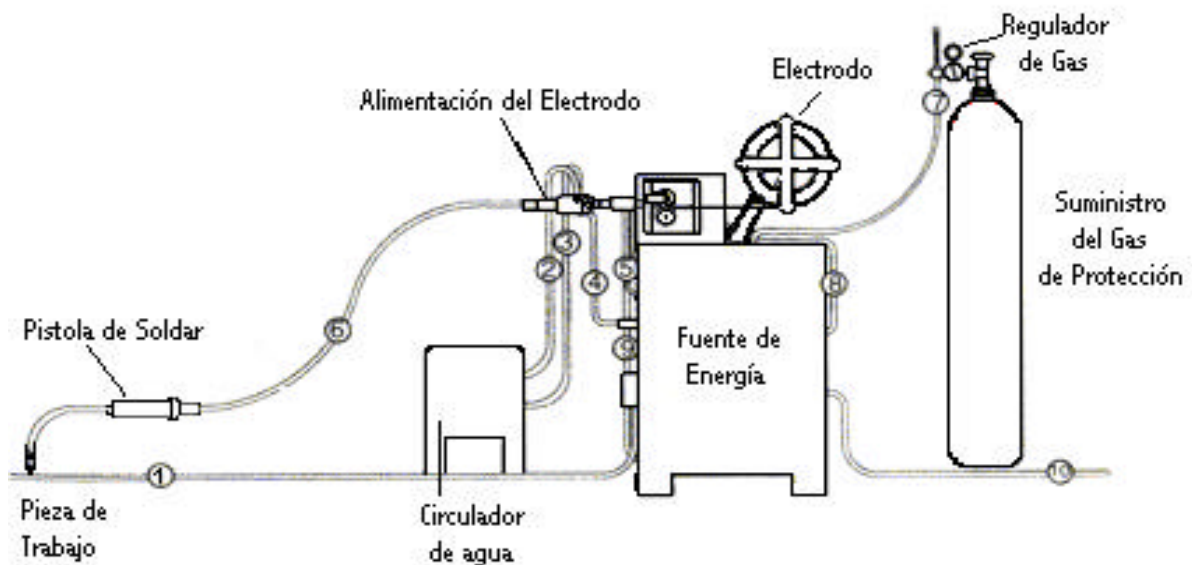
Diagrama del equipo para soldadura por arco de metal y gas.
